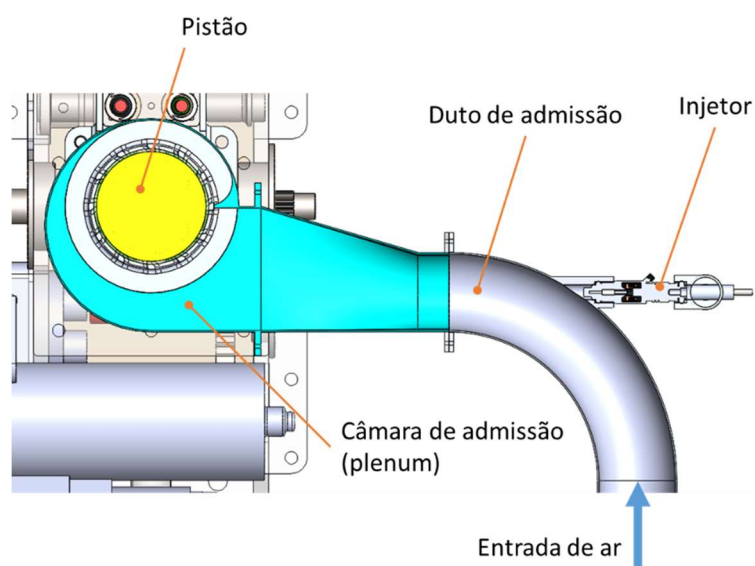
Montagem do motor em SolidWorks® e seus principais componentes.
